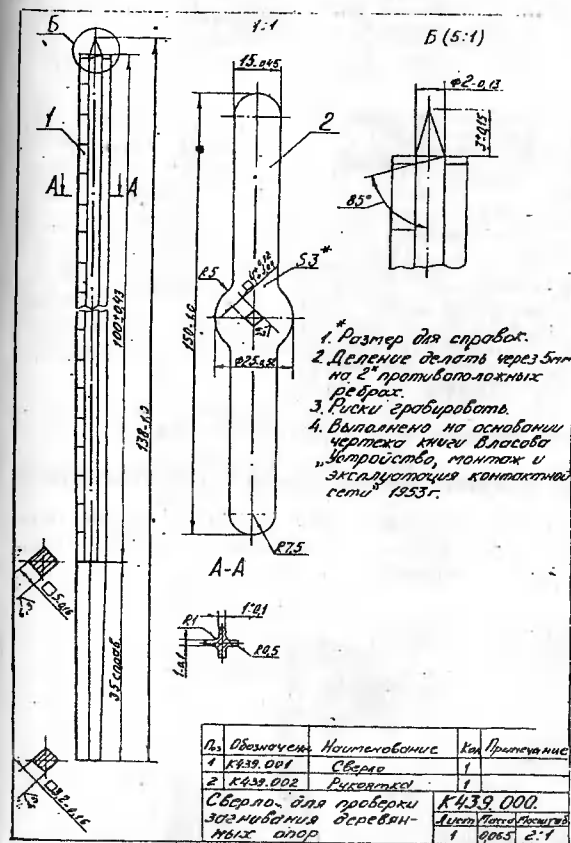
Рабочие чертежи изготовления сверла для проверки загнивания деревянных опор:
